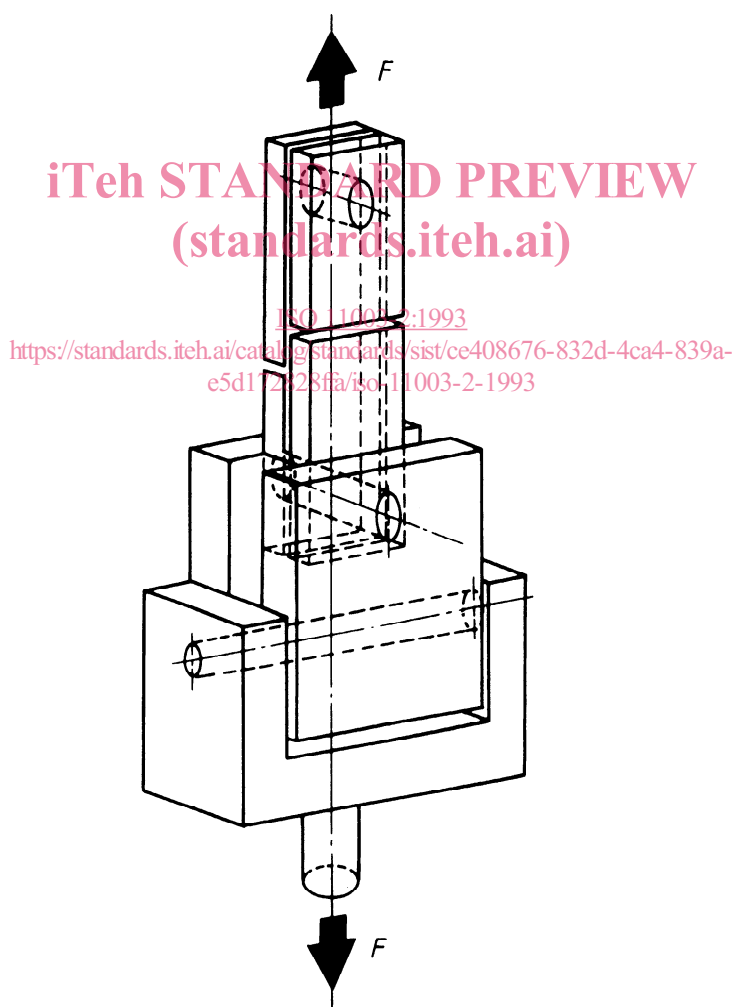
Dispositif de fixation de l'éprouvette sur la machine d'essai (montage à cardan)
